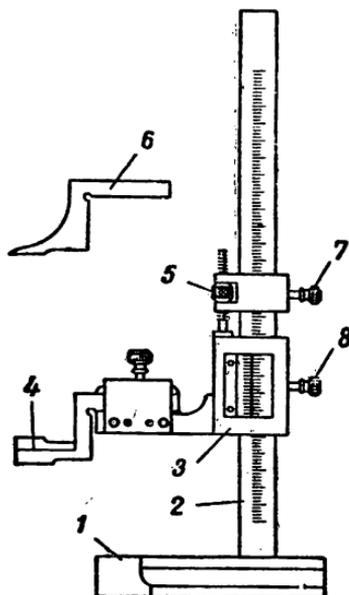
Штангенрейсмус: 1—подставка; 2—штанга; 3—рамка с нониусом; 4—сменная ножка для измерения высоты; 5—микрометрическая подача рамки; 6—сменная ножка для разметки; 7—винт ползуна; 8—закрепительный винт рамки.
